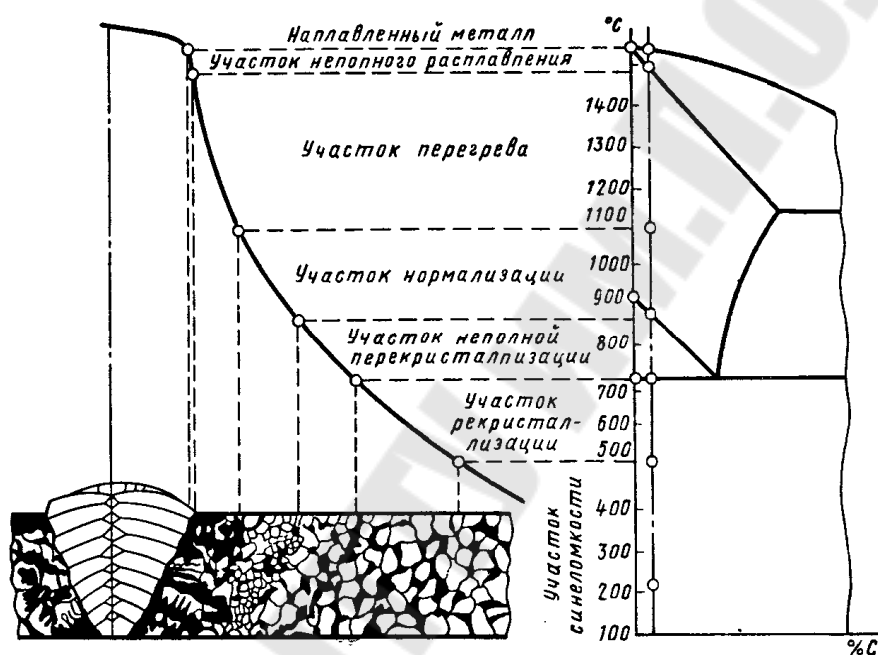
Структура зоны термического влияния сварочного шва
